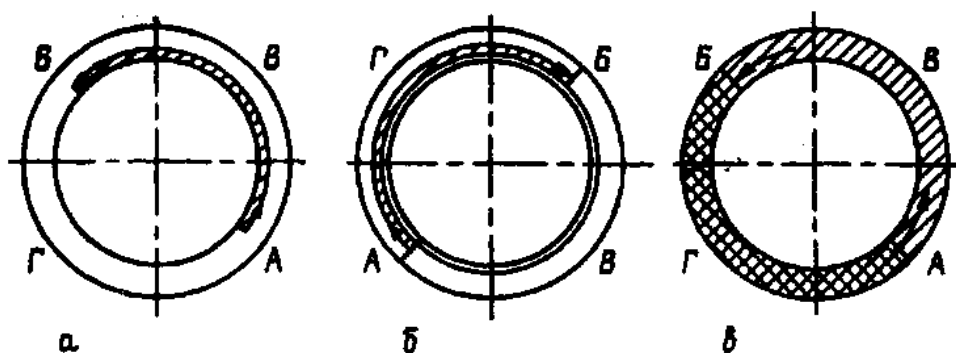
Порядок сварки стыка труб с поворотом на 90°
